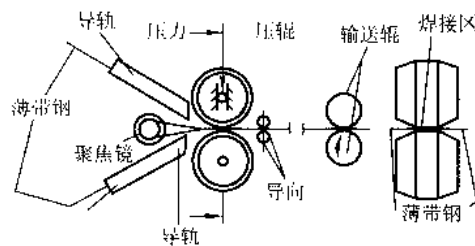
采用激光焊接对薄钢带焊接示意图
